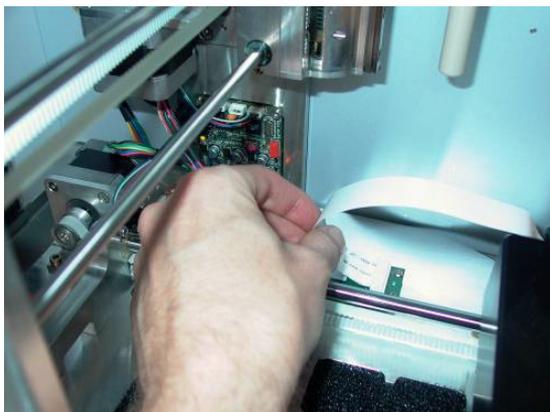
显示将电缆固定到 PCB 固定器的特写视图。
